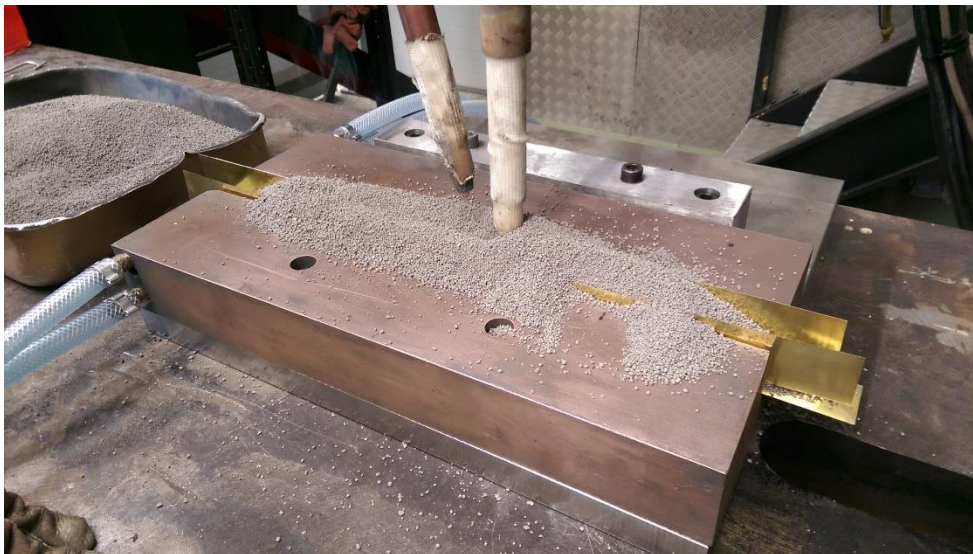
Realización de prueba de soldadura 2-1 con SAW.
